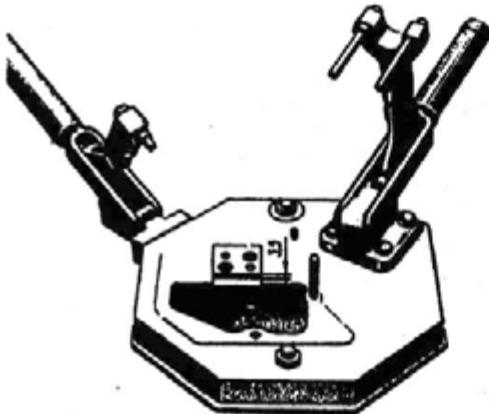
Приспособление для разборки и сборки механизма переключения передач
